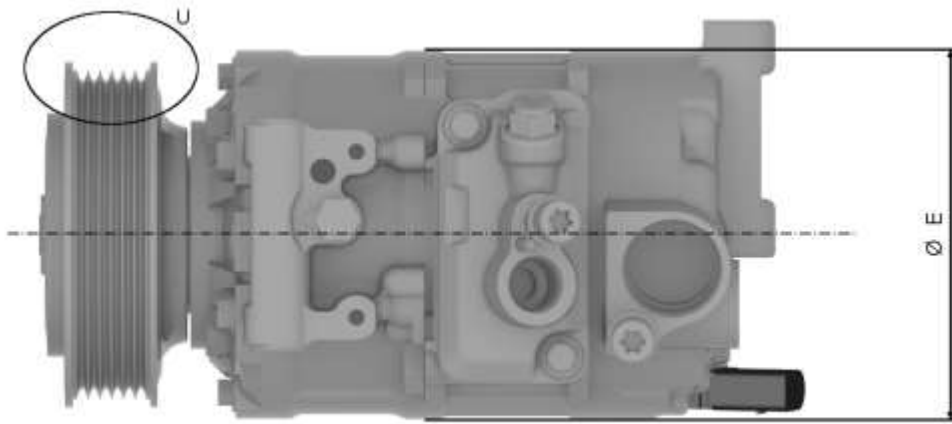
Dimensions du compresseur de fluide frigorigène, vue de dessus (exemple DENSO-7SEU17)
